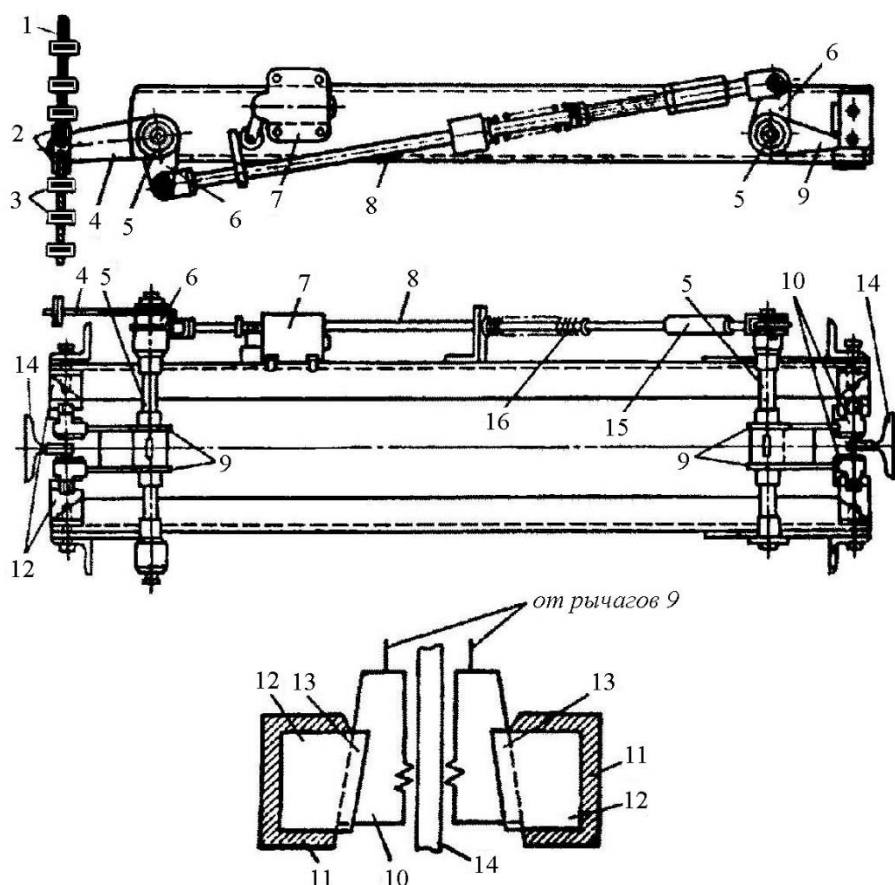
Приводной механизм ловителей резкого торможения.
